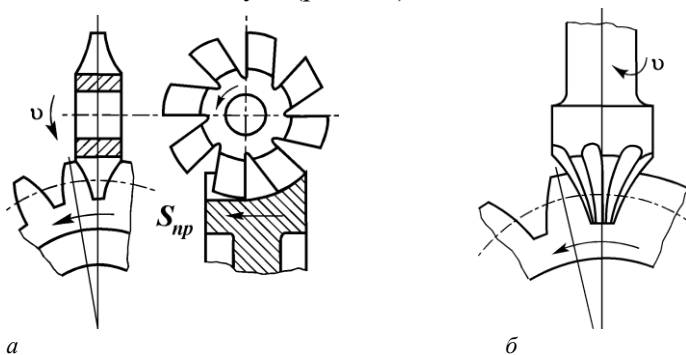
Схемы нарезания зубчатых колес модульными фрезами [5]:
